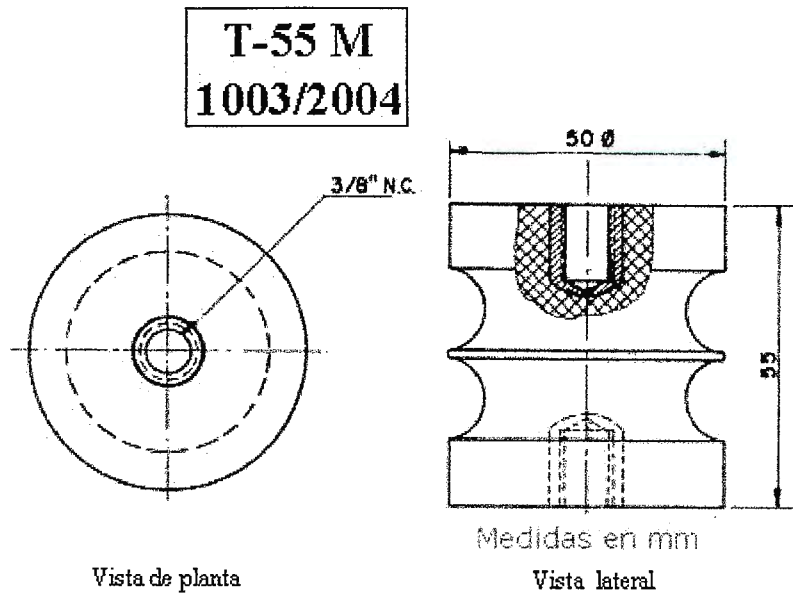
Aislador T-55 para montaje de barras de hasta 80x10mm
